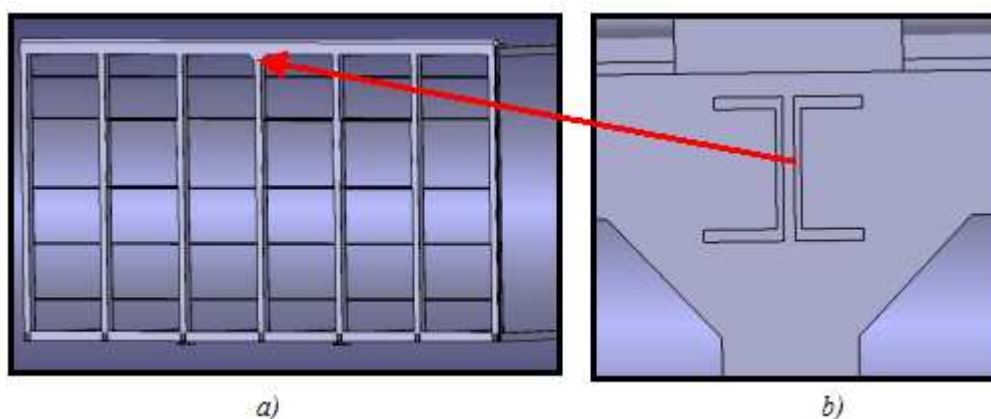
Estructura móvil. (Refuerzo central) a)Localización del refuerzo. b)Detalle de la escuadra en la estructura
